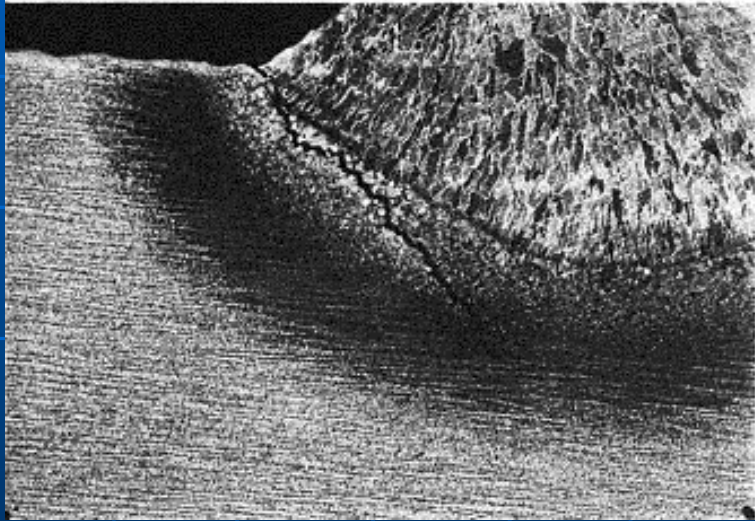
Fischaugen im Schweißgut (4:1)
